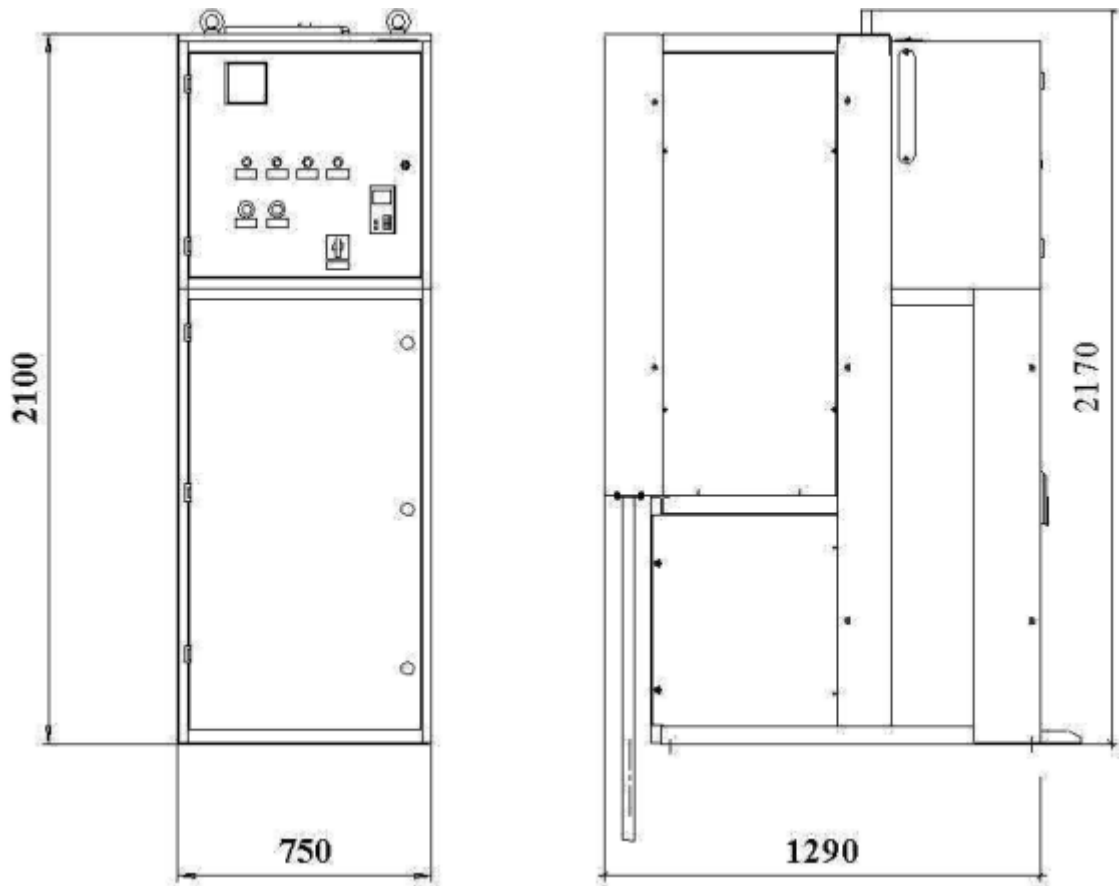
Габаритные размеры камер К-64-МЧ внутренней установки
